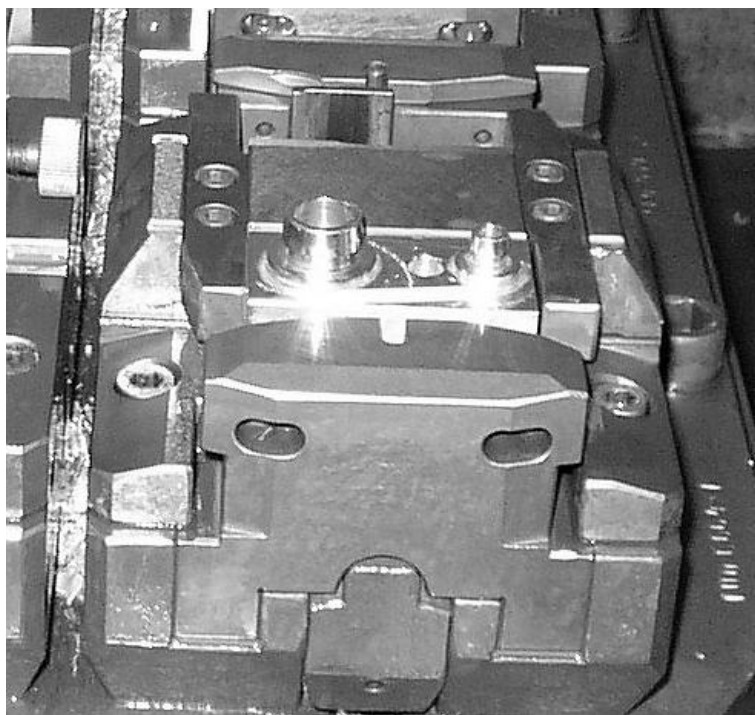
Po obrobení spodní roviny obrobku 1. upnutí
